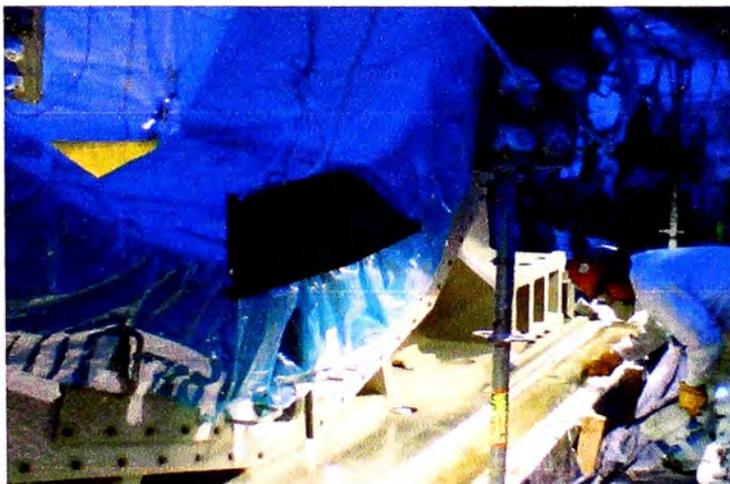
Montaje de cojinetes principales, culminado el grout epóxico, (Proyecto Antapaccay).
